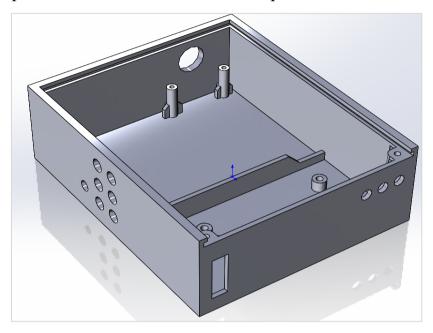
Общий вид нового корпуса, часть 1
